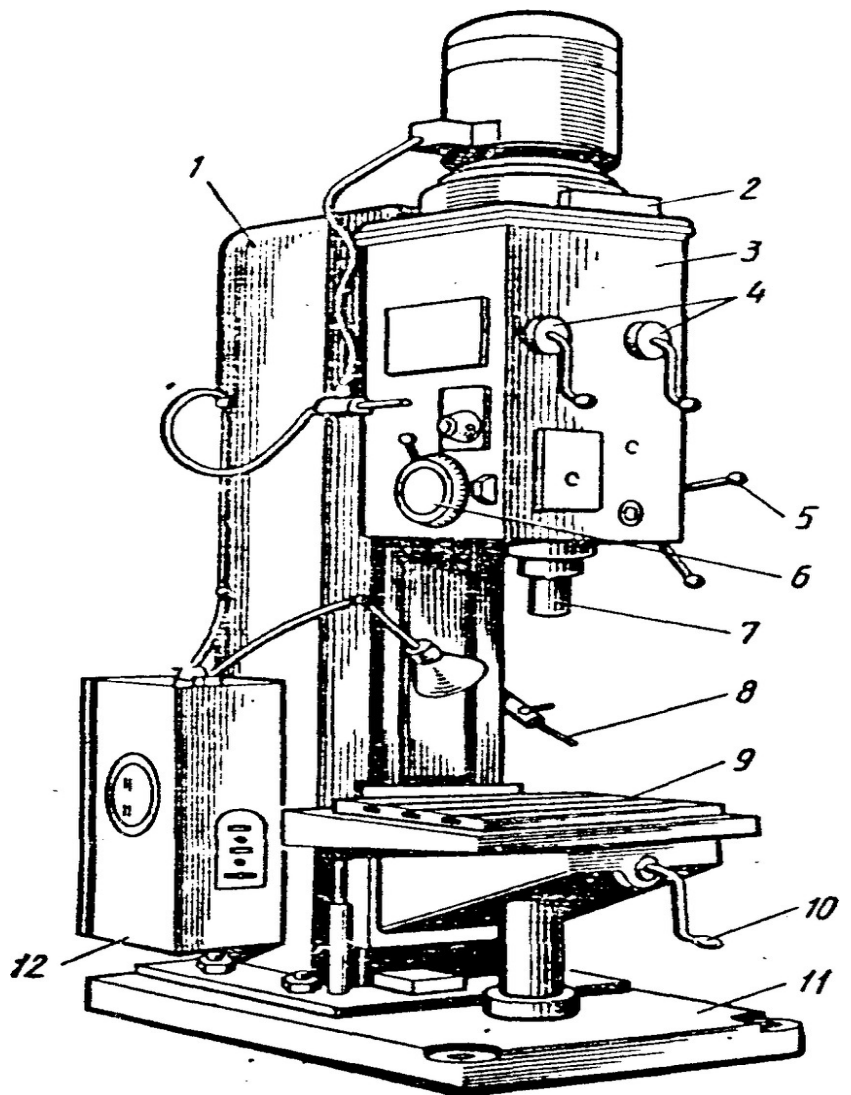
Вертикально-свердильний верстат 2Н125
